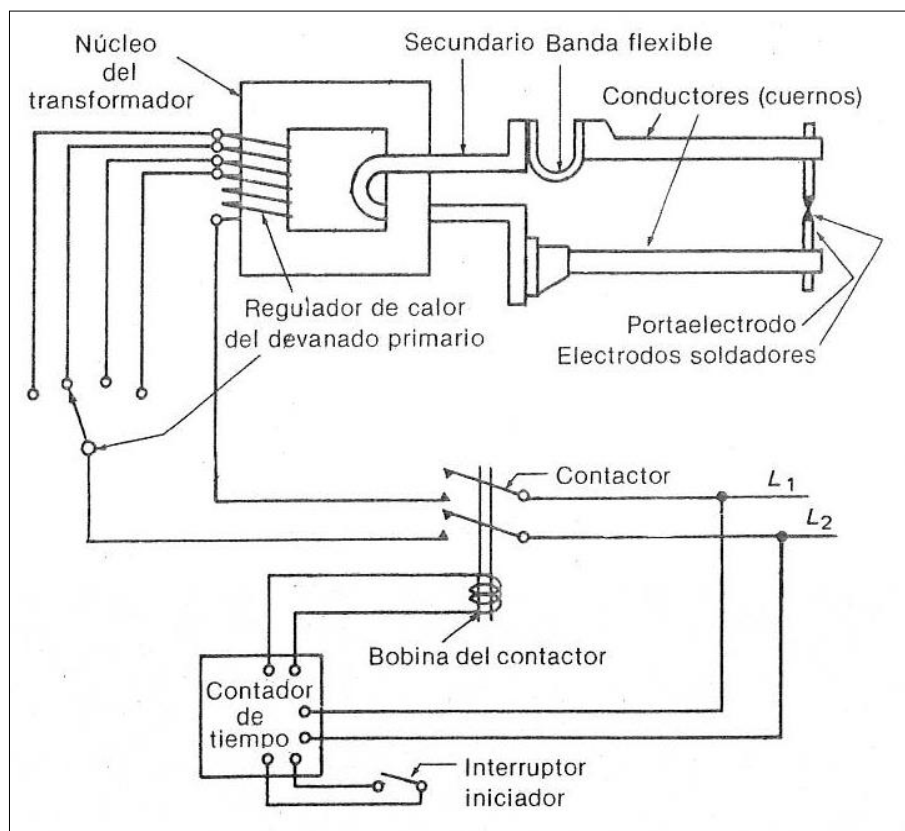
Esquema de máquina de soldadura por resistencia de corriente alterna monofásica.
